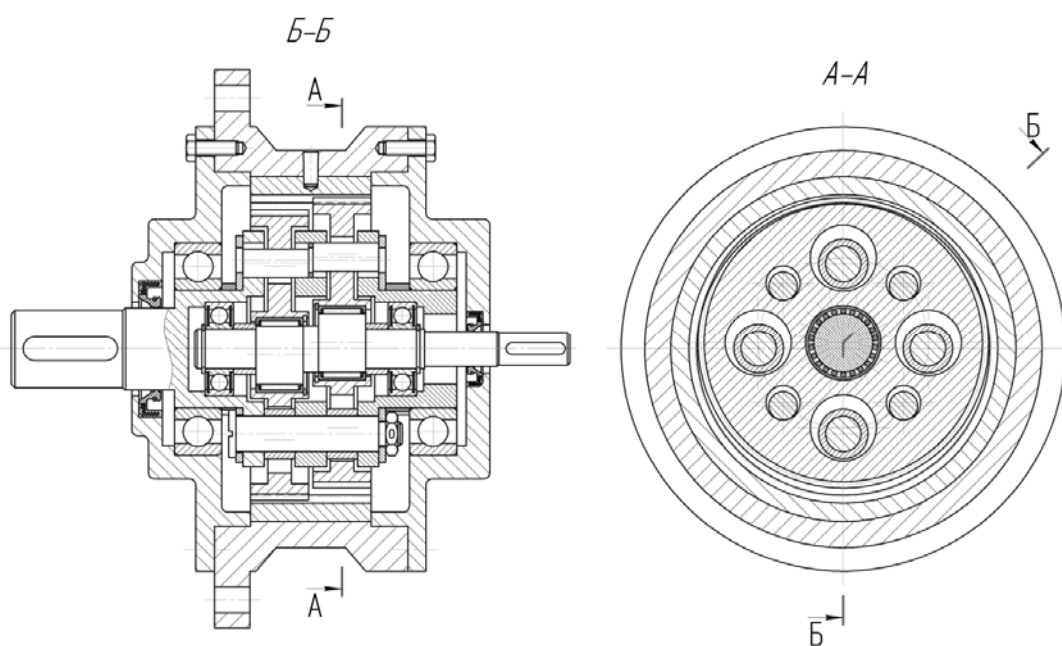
Вариант планетарной передачи с внутренними зацеплениями колес и роликовым механизмом снятия движения с сателлитов (пат. 2445529 Рос. Федерации: МПК F16Н1/32.
